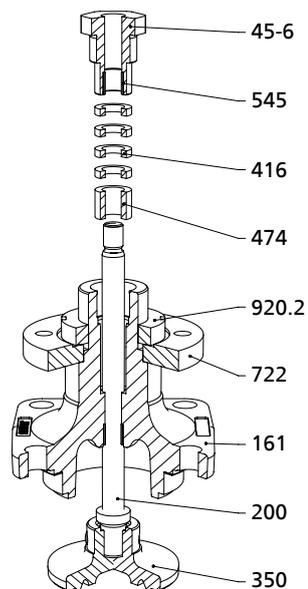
Desmontaje de la empaquetadura del prensaestopas de grafito
